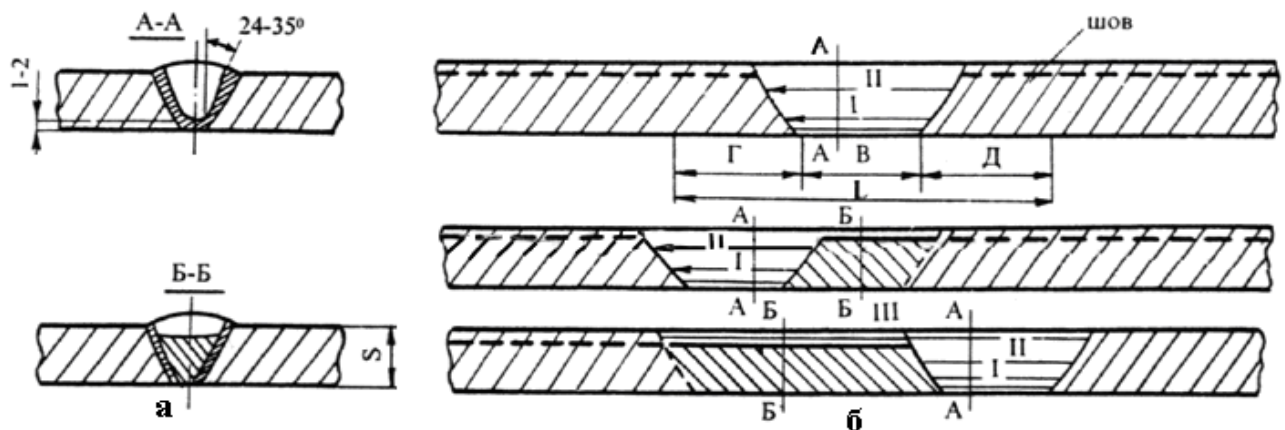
Подготовка трещин (*а*) и отверстия (*б*) к заварке
